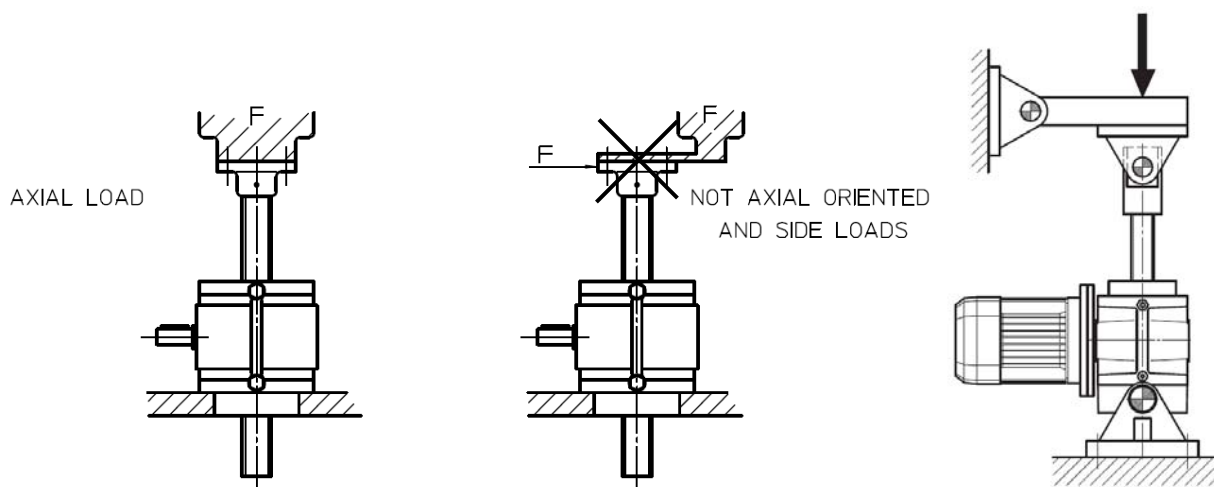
Installation des Kugelgewinde-Hubgetriebes
